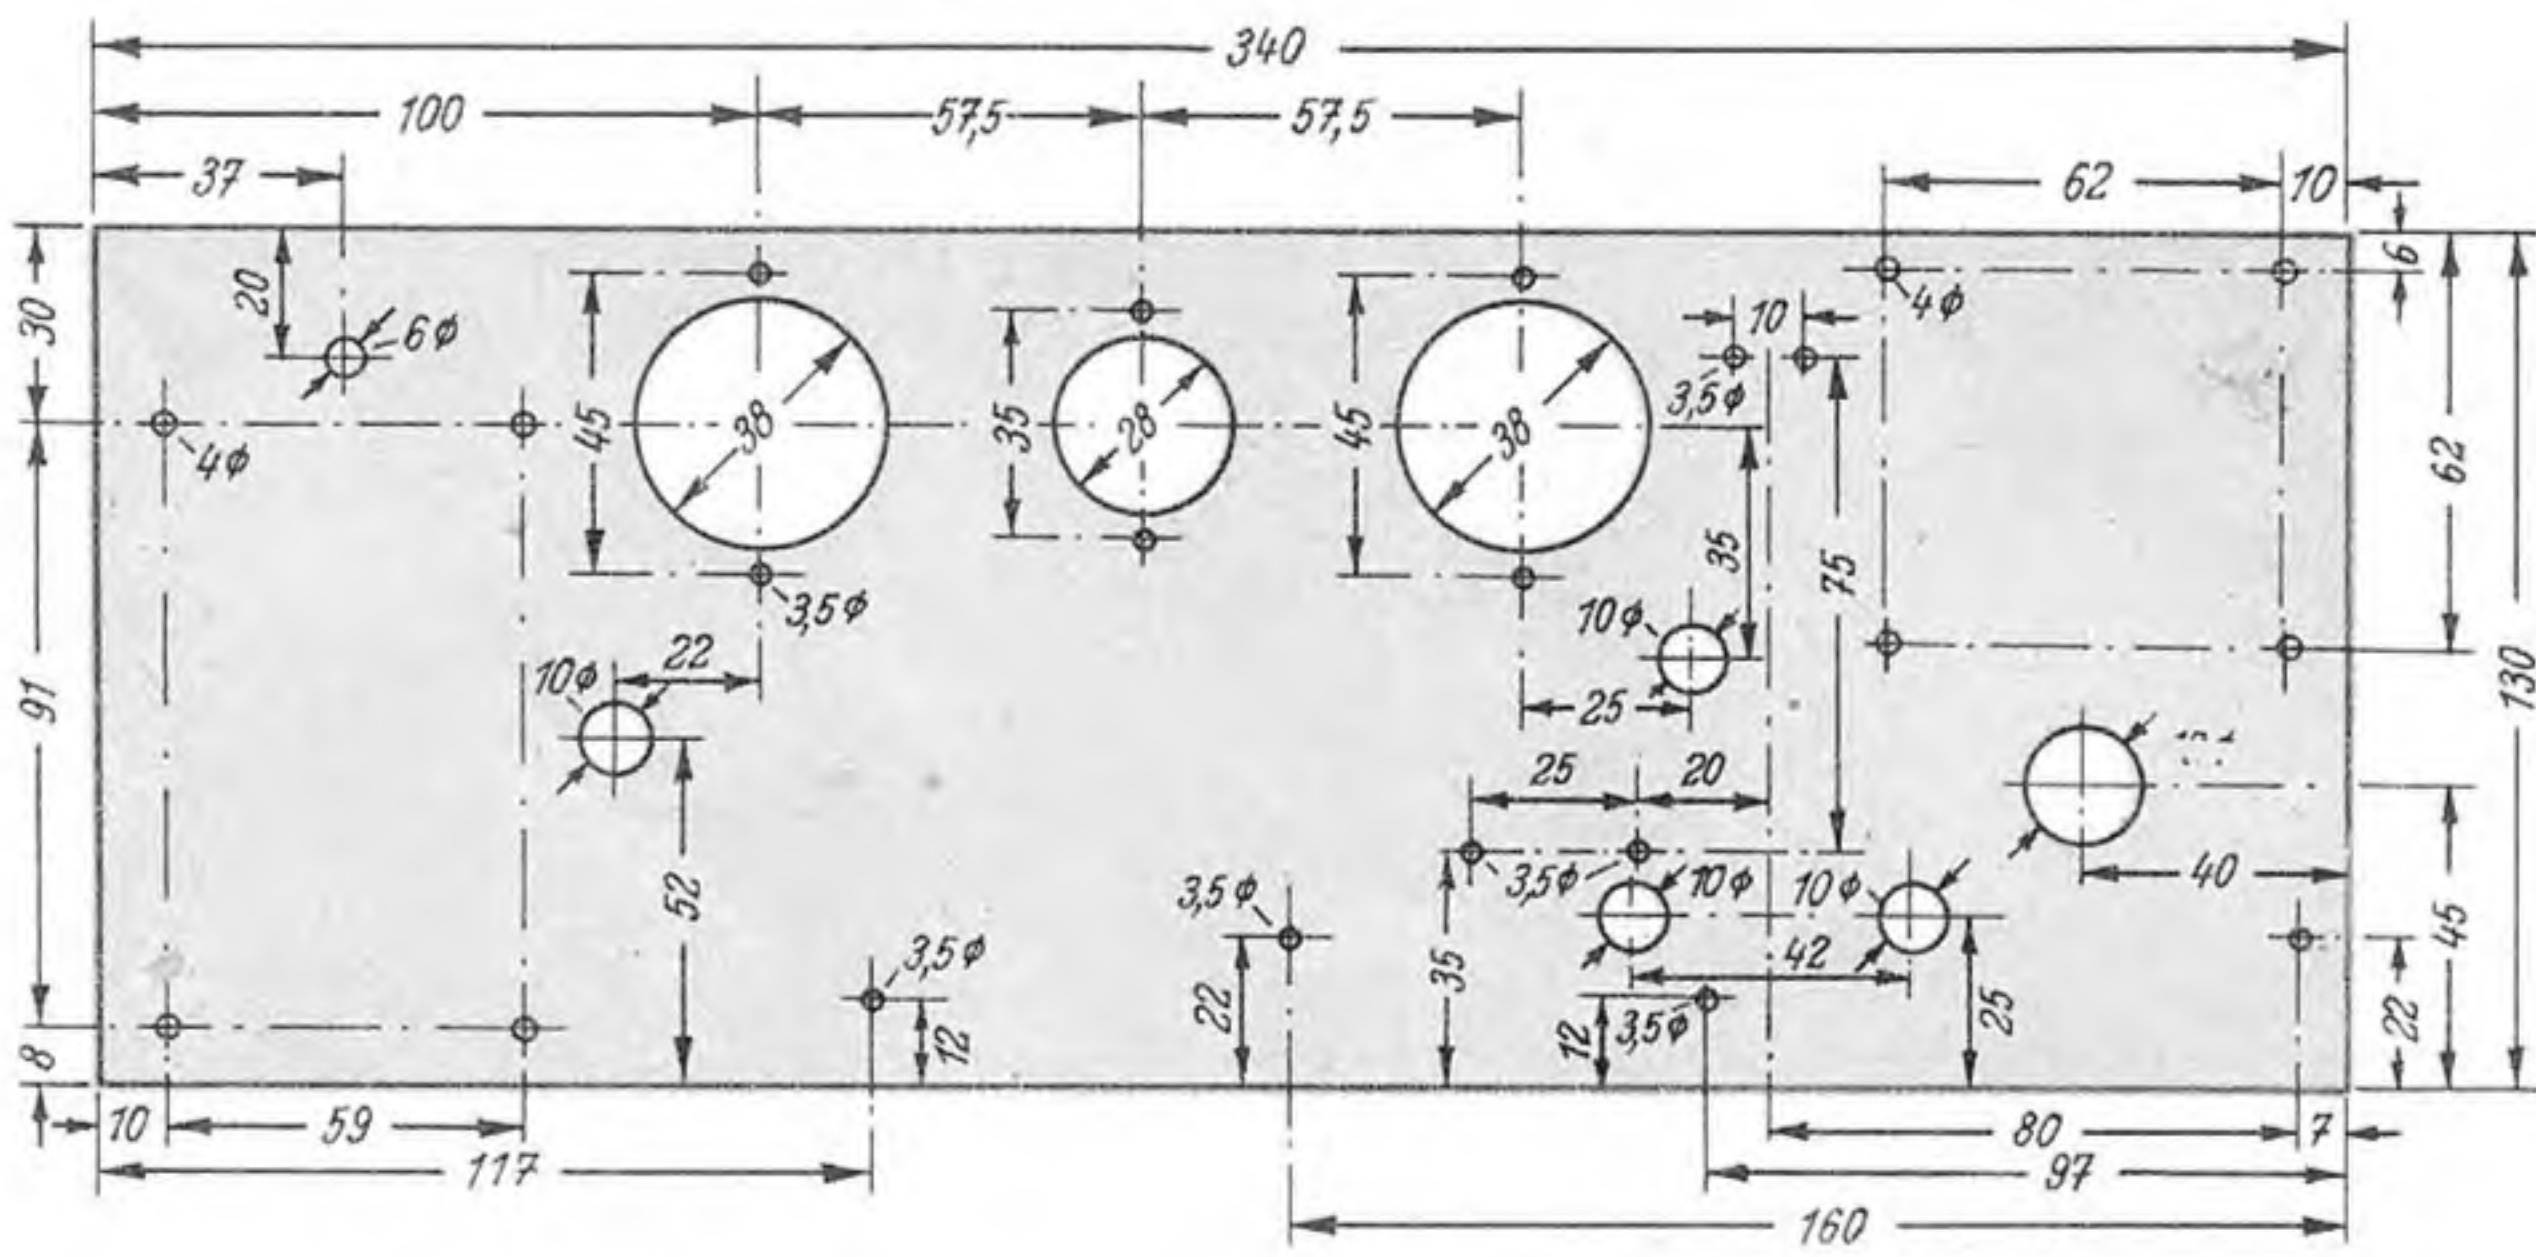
Chassisaufriß des Ausführungsbeispiels
